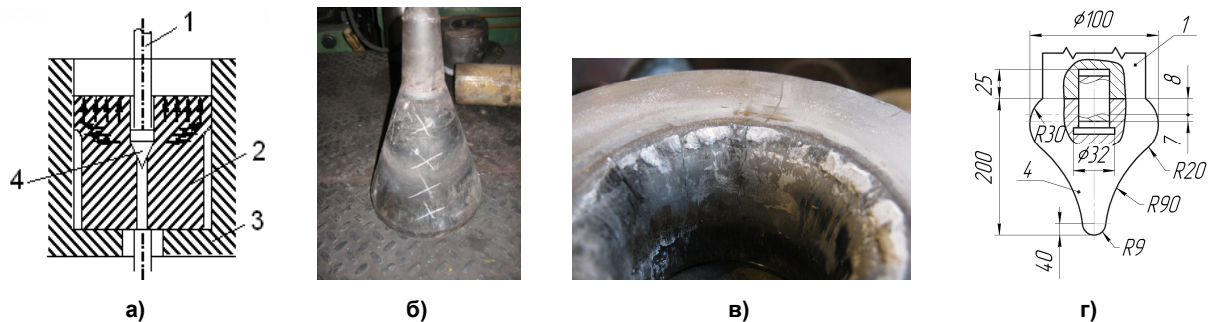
Схема технологического процесса экспандирования трубной заготовки (а); картины износа экспандера (б), контейнера (в); оправка (г) вертикального прошивного пресса 12 МН фирмы SMS MEER трубопрессовой линии. 1 – стержень (игла); 2 – трубная заготовка; 3 – контейнер; 4 – экспандер (оправка)
